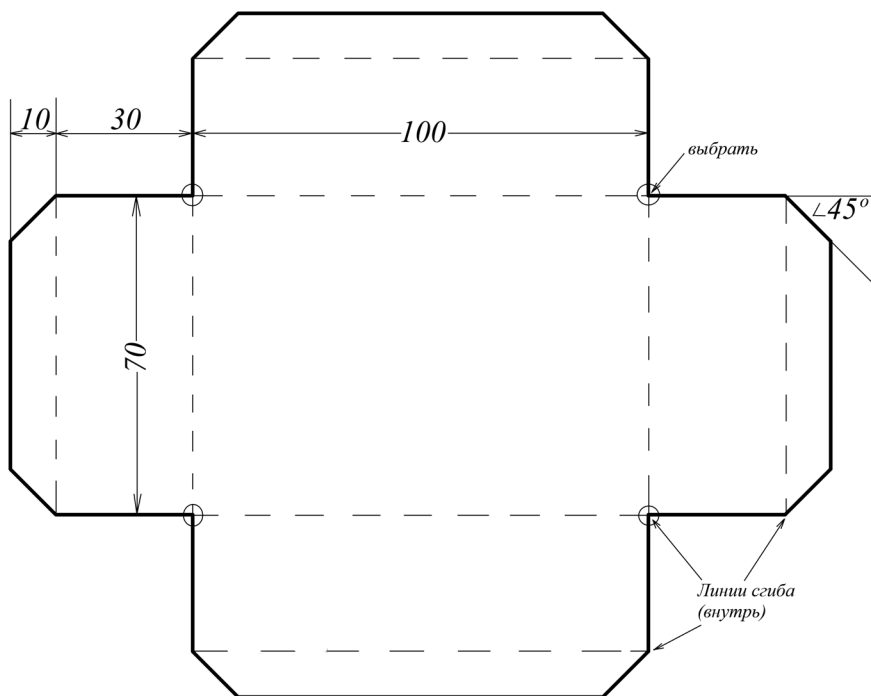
Развёртка корпуса лабораторного УЗЧ.
